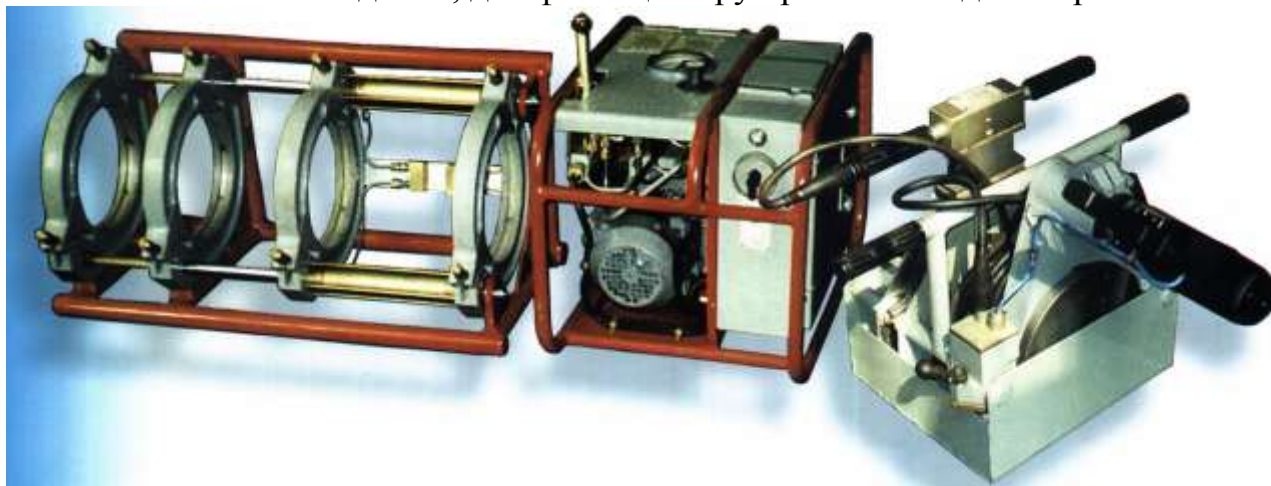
Установка для сварки полимерных труб встык нагретым инструментом при горизонтальном расположении осей
